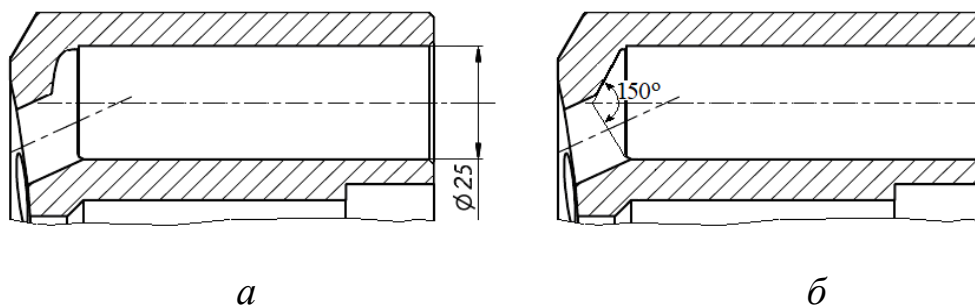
Форма торцевої поверхні циліндрових каналів БЦ
